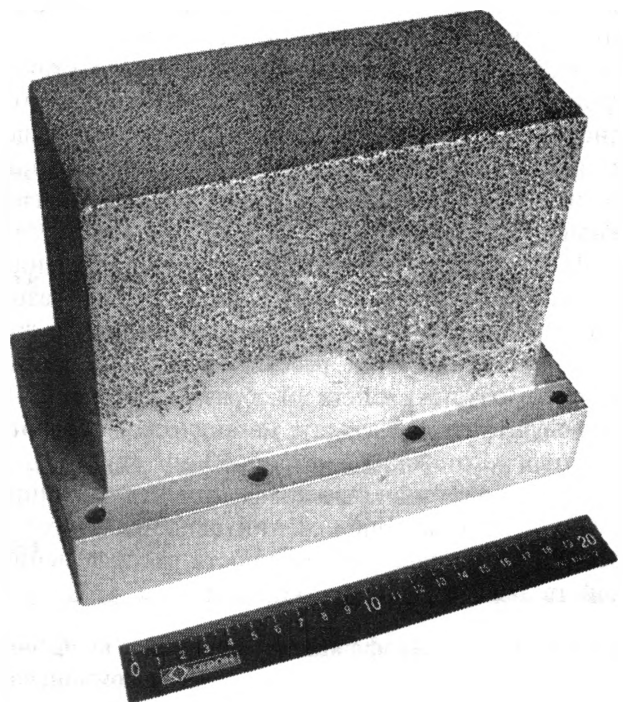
Деталь «Корпус глушителя компрессора» из сплава АК12
